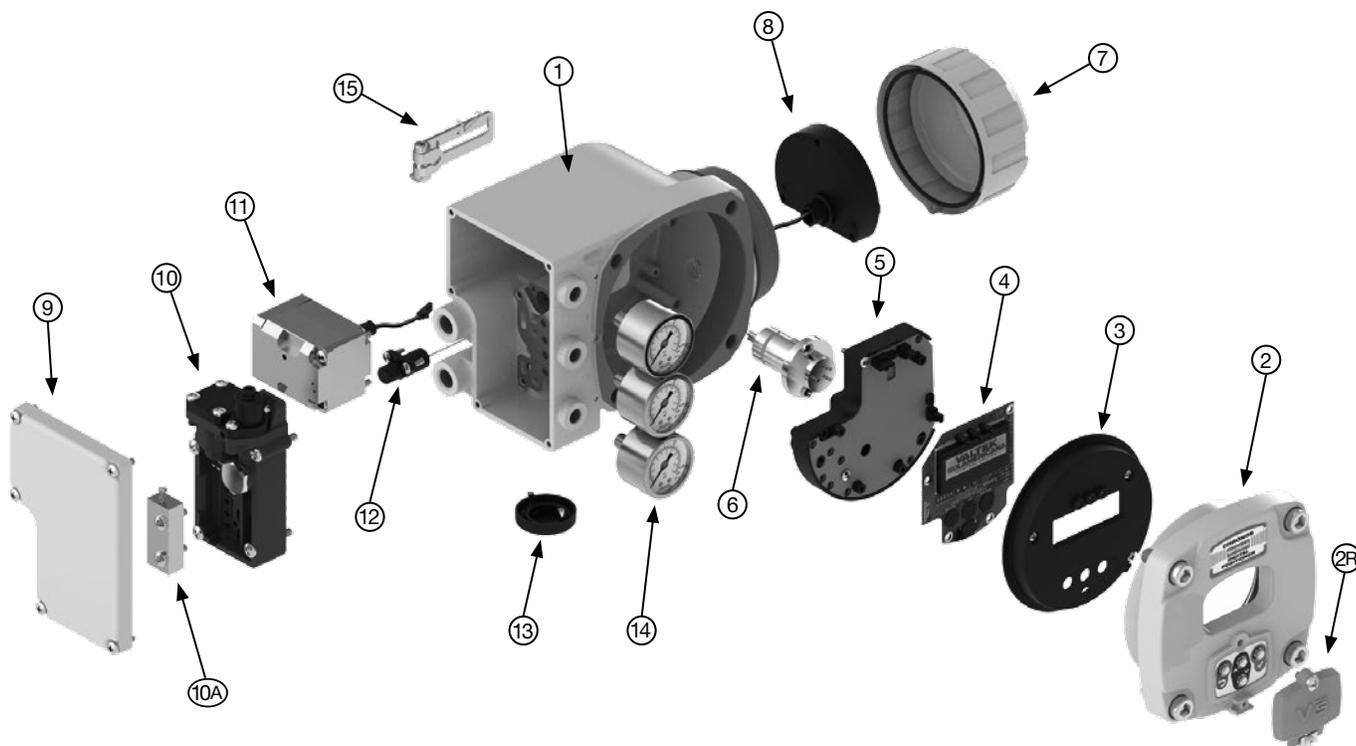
Vista explodida do Posicionador Chronos IDP7600
